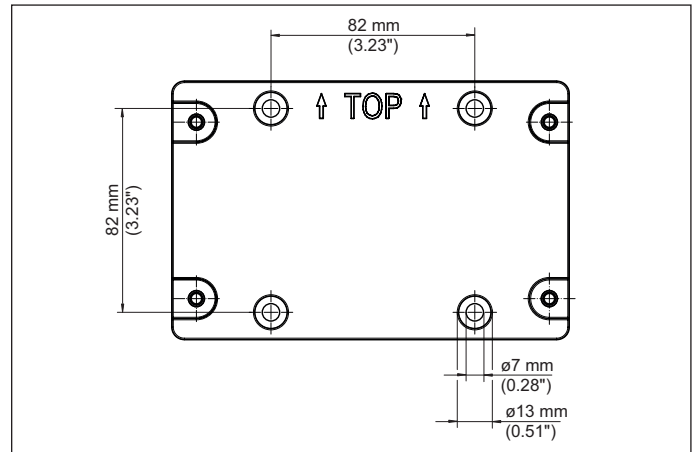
Montageplaat voor wandmontage (VEGAMET 841, 842)
